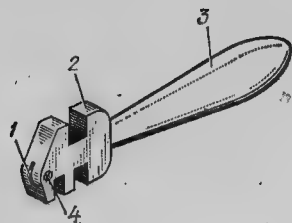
1 — ролик; 2 — державка; 3 — ручка; 4 — колпачок; 5 — барабанчик
